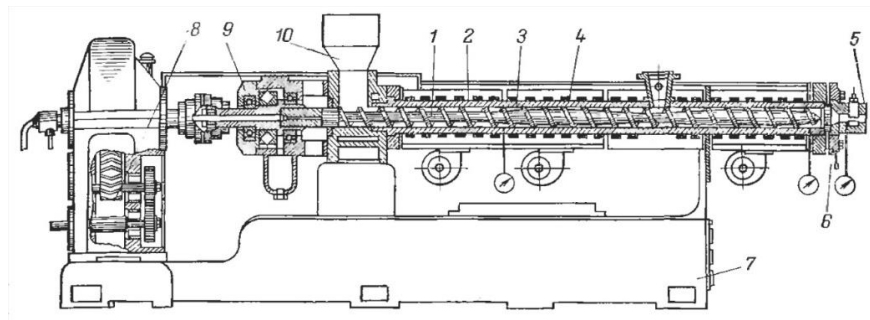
Одношнековый экструдер: 1 – шнек; 2 – корпус; 3 – гильза материального цилиндра; 4 – нагревательные элементы; 5 – экструзионная головка с профилирующим инструментом; 6 – адаптер; 7 – станина; 8, 9 – редуктор и блок упорных подшипников; 10 – бункер
